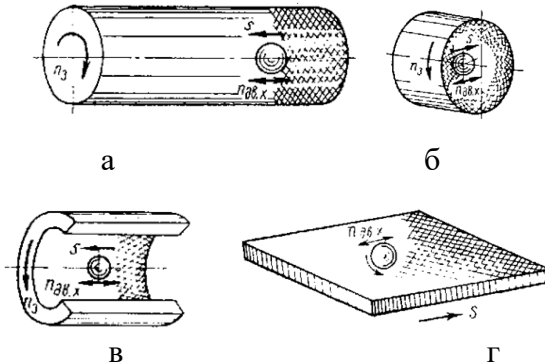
Різні форми поверхонь деталей з регулярним мікрорельєфом
